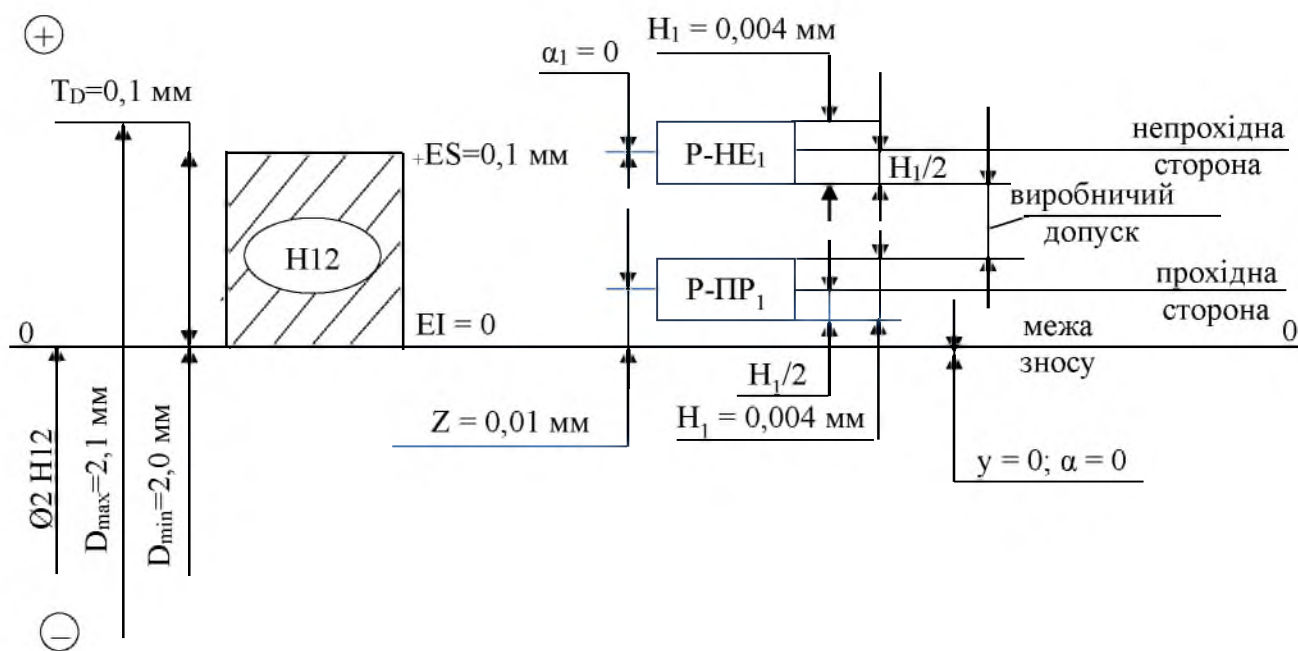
схема розташування полів допусків калібр-пробки
